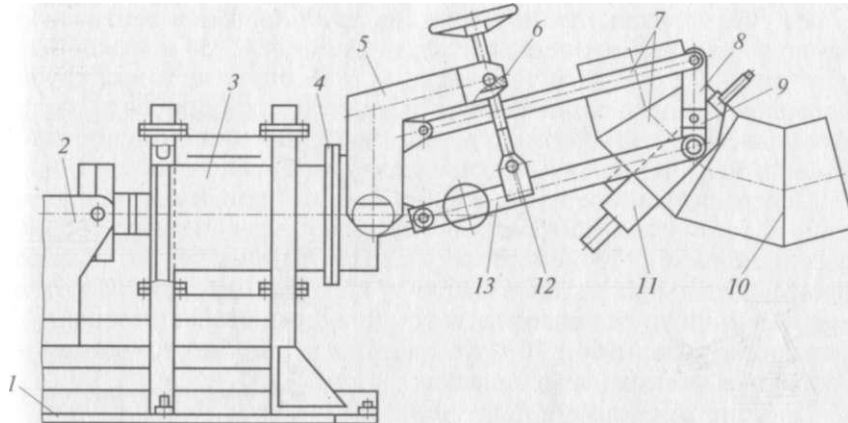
Установка УСО-1420 для сварки отводов с $D = 400 \dots 1400$ мм:
